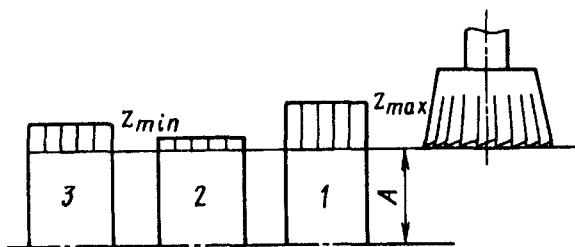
Фрезерование заготовок с разной величиной припуска
